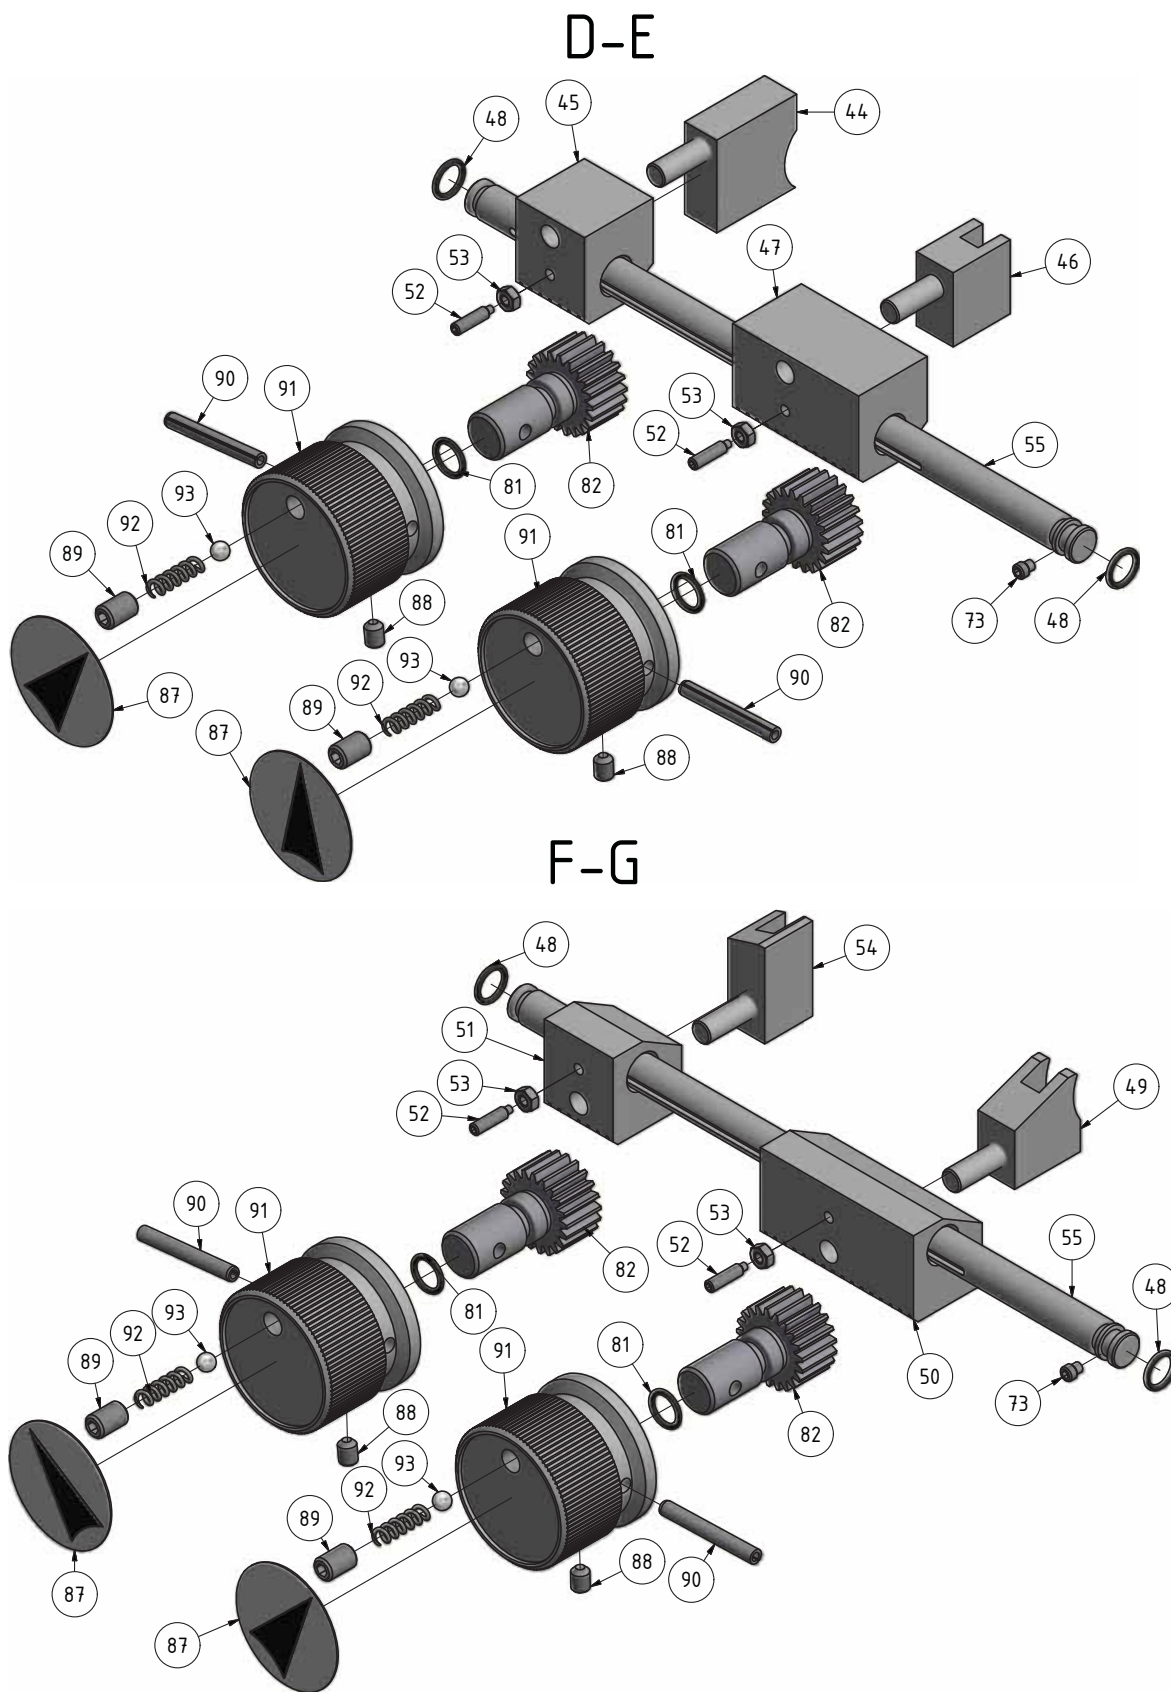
Vorschubgetriebe 6-6 - Feed gear 6-6
